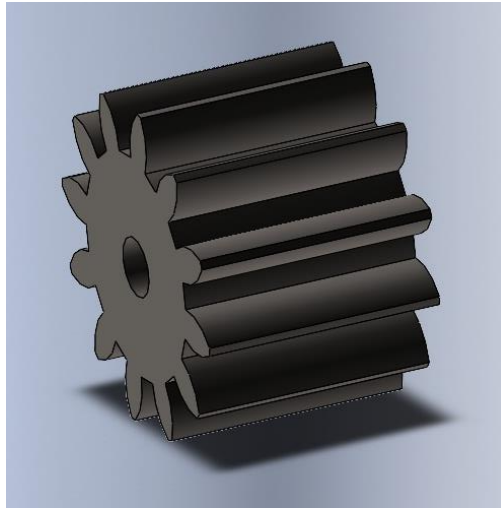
Diseño Engranaje acoplado en eje de motor stepper de Cuello de Robot
